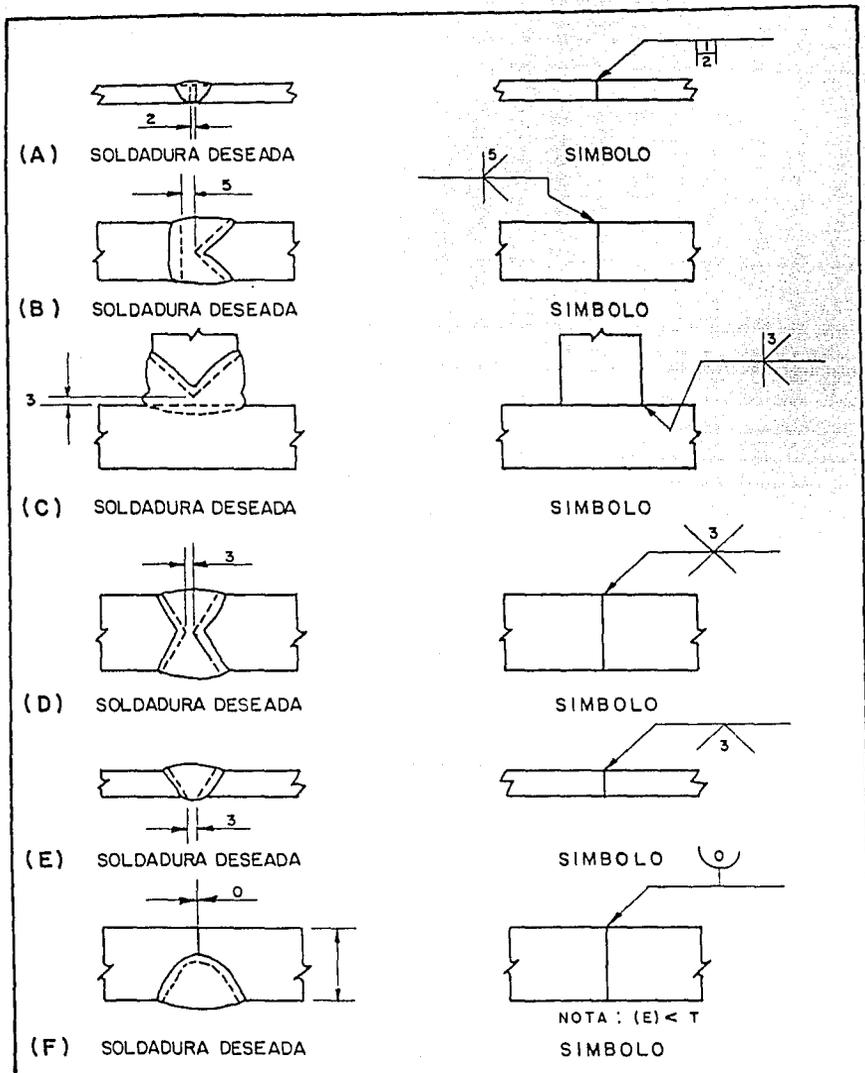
DESIGNACION DE SOLDADURAS A TOPE DE RAIZ ABIERTA
